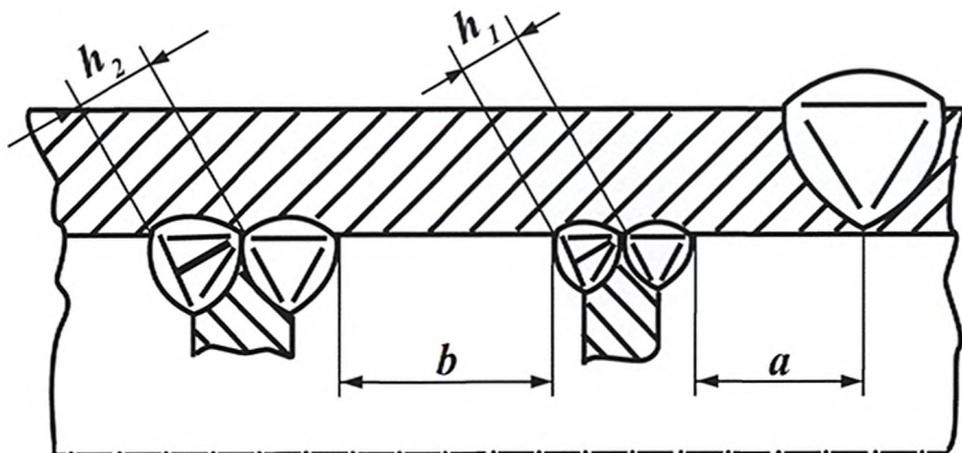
Расположение сварных соединений приварки деталей к оборудованию и трубопроводам
